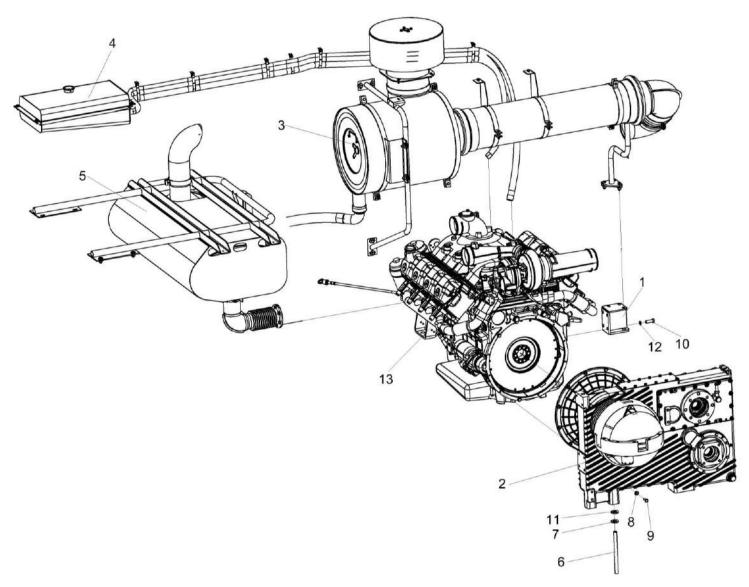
Установка двигателя ОМ 502LA КВК 0150000 (установка главного привода, воздухоочистителя, бачка расширительного и глушителя)
